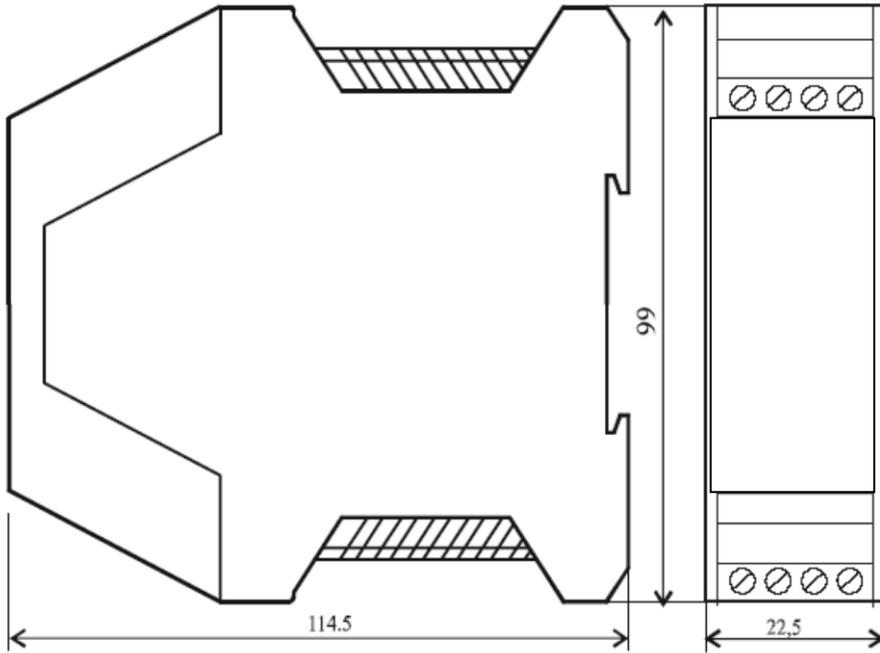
Внешний вид, габаритные и установочные размеры преобразователей измерительных S2
